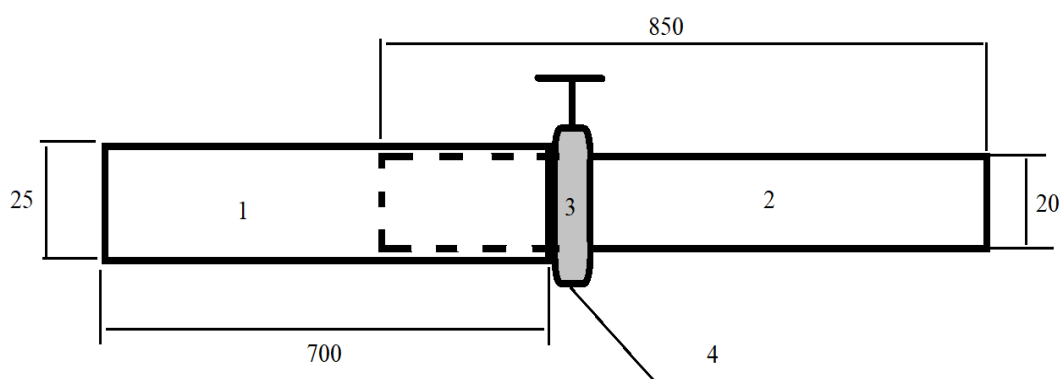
Схема конструктивного решения сборки опорных конструкций для закрепления паутинной сети: 1 – алюминиевая труба D 25 мм; 2 – алюминиевая труба D 20 мм; 3 – опорный омут; 4 – точка упора трубы D 20
